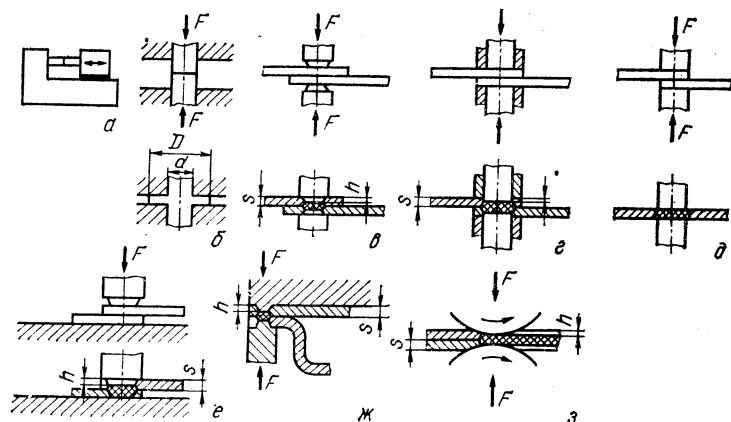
Принцип и схема сварки: а — принцип; б — сварка встык; в—е — сварка внахлестку; ж, з — шовная сварка
